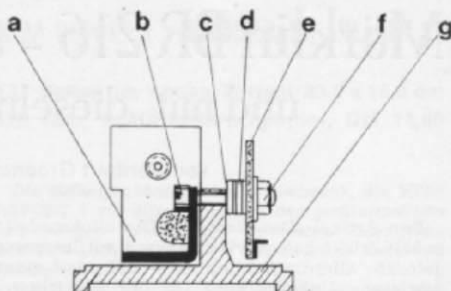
Stirnansicht (M 1:1 für H0) des an das Chassis angeschraubten Zepp-Motors nebst „Zubehör“. Es bedeuten: a = Zepp-Motor mit Grundplatte, b = M2-Zylinderkopfschraube 15 mm lang, c = Lötkontaktblech (Anschluß an Zepp-Motor), d = Lötkontaktblech (Anschluß an Dioden-Lötöse, unten), e = Märklin-Lötstütze Nr. 22179, f = Vorlagescheibe mit M2-Sechsmutter, g = Fahrgestell mit Montagestütze.
